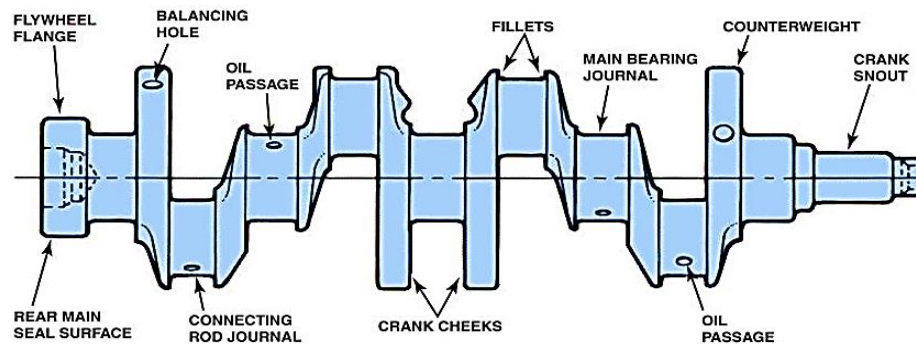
Continental O – 200 – A Nitrided Crankshaft
